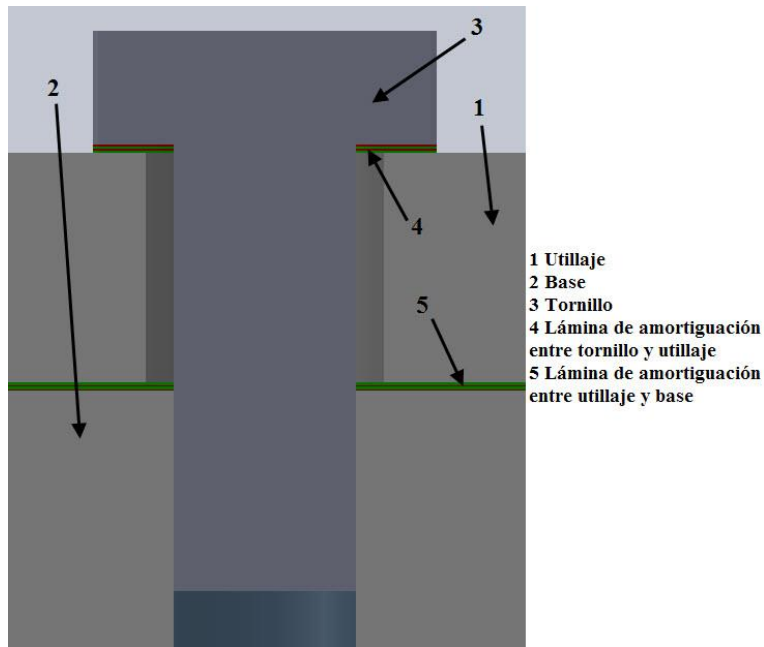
Vista de la sección del tornillo de anclaje del utillaje
